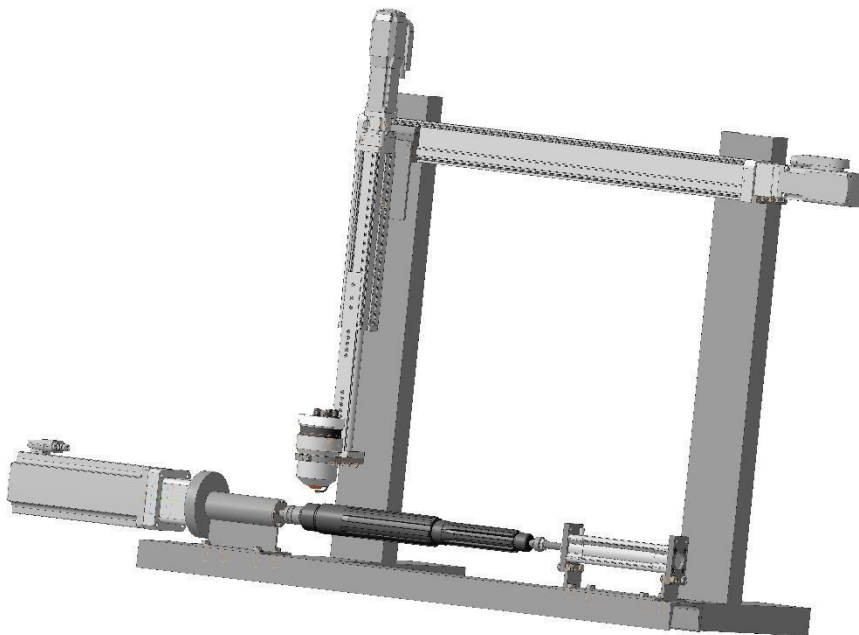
Установка з ЧПК для автоматизованого відновлення деталей типу «вал»
